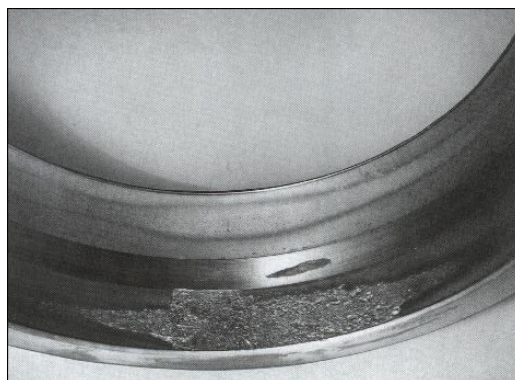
Desconchado del aro exterior de un rodamiento de rodillos a rótula que ha sido montado en un alojamiento ovalado.
